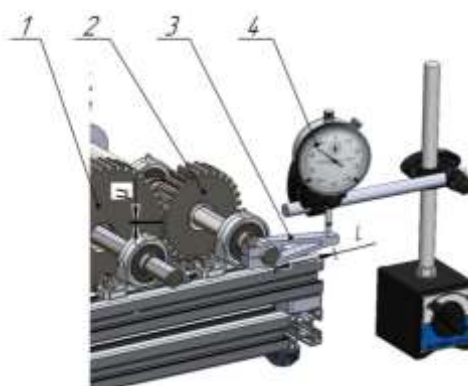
Схема контроля бокового зазора в зубчатом зацеплении
